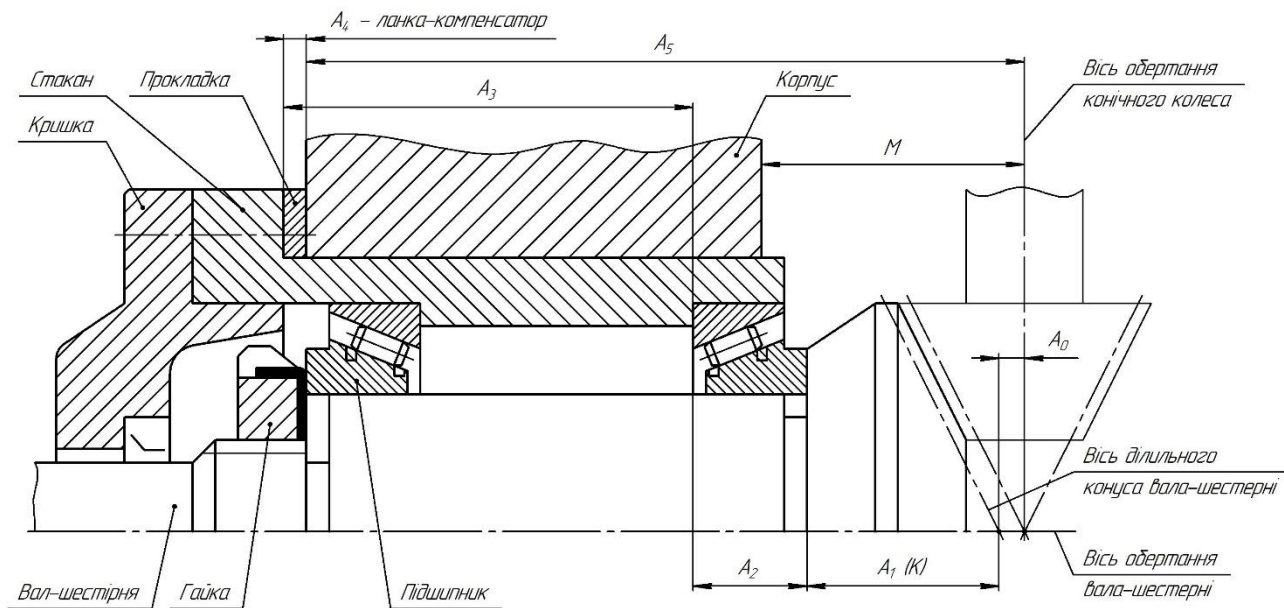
Схема розмірного ланцюга, що визначає точність збігу вершин ділильного конуса вала-шестерні з віссю обертання кінцевого колеса
